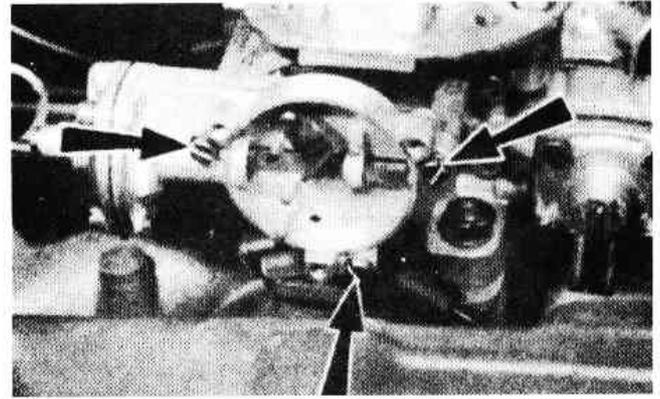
Винты крепления автоматической заслонки (Разд. 27)
